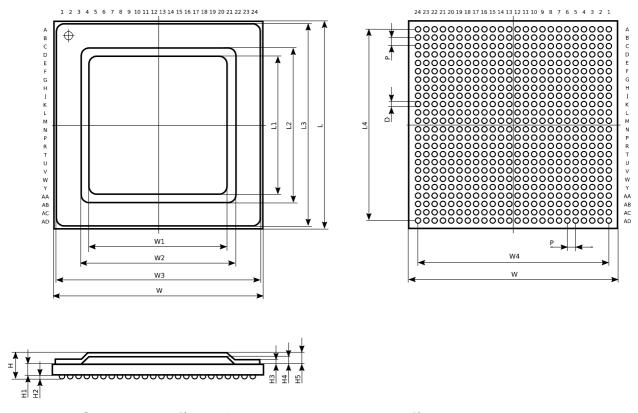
Схематический чертёж корпуса микросхемы Байкал-Т1
